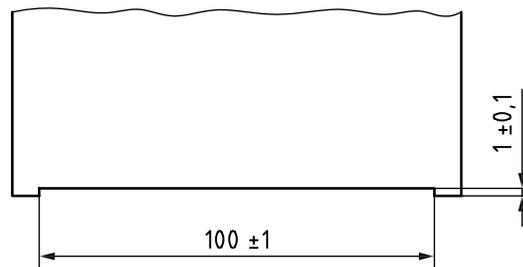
Dimensions de l'ouverture de l'applicateur d'adhésif
